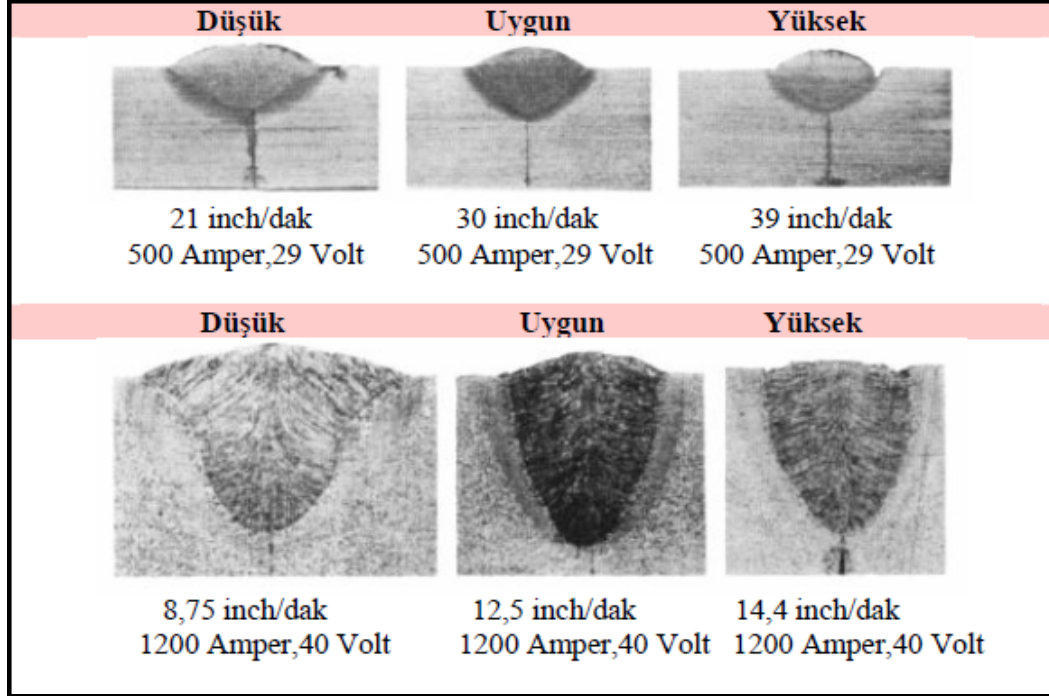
Tozaltı ark kaynak akımının, dikiş geometrisine ve nüfuziyete etkisi [29].
